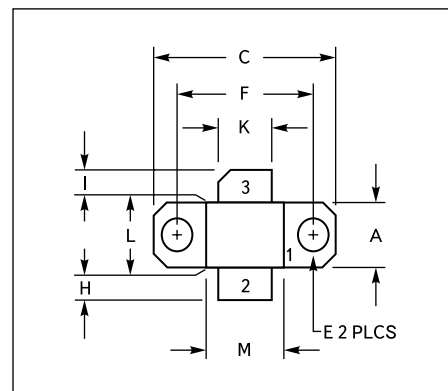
Размеры корпуса транзистора IB2729S170: длина "M" = 320 мил (8 мм); ширина "A" = 250 мил (6,25 мм)
